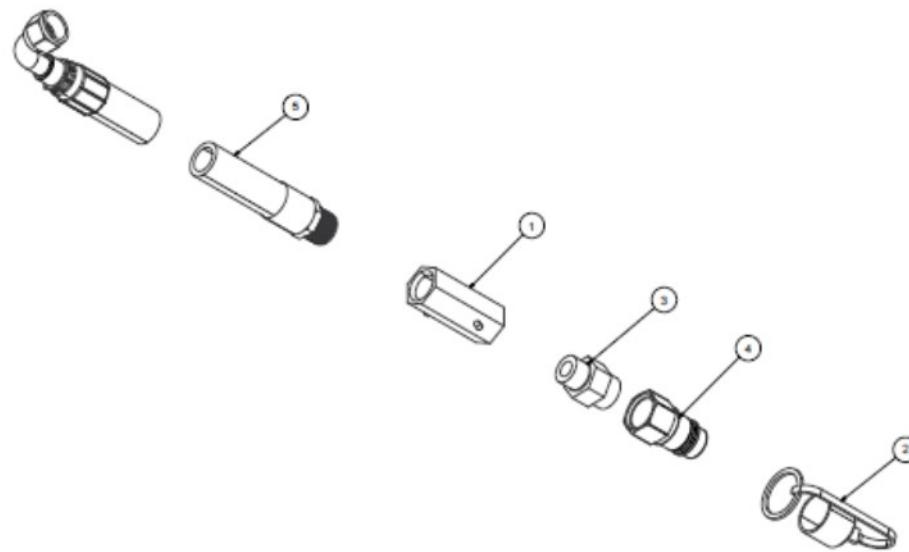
Чертеж сборки гидравлической возвратной линии– 815823
